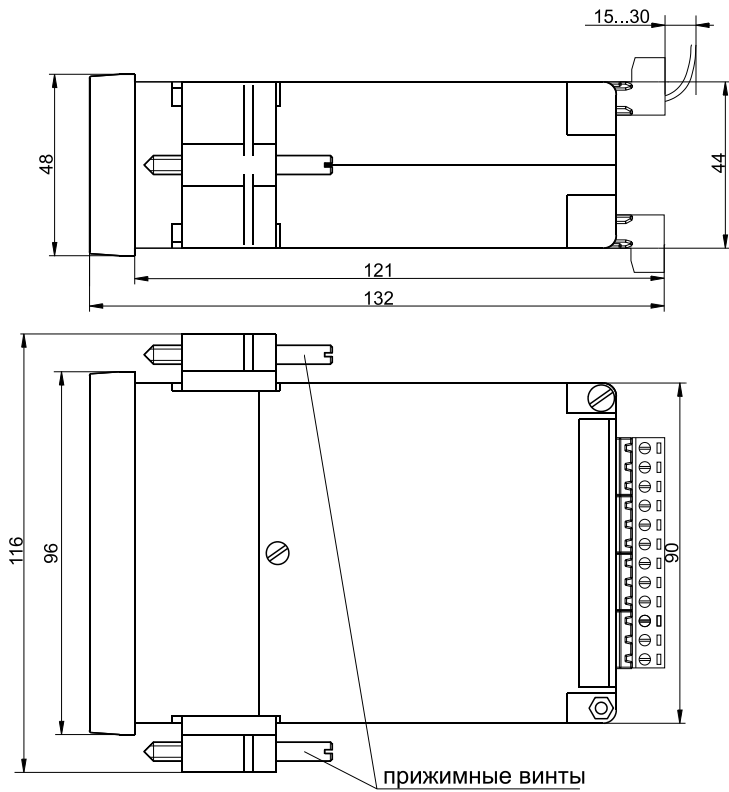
Габаритные размеры прибора МЕТАКОН-6305
